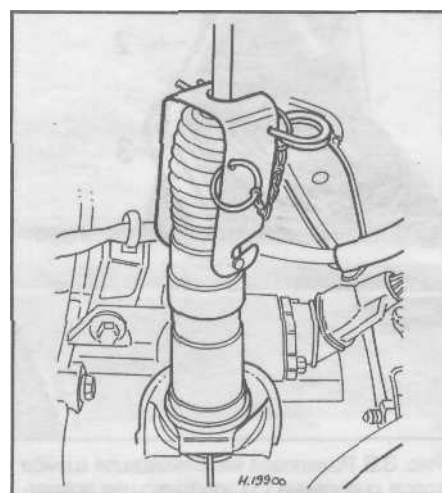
Механизм автоматической регулировки троса сцепления сжатый при помощи приспособления VW 3151
